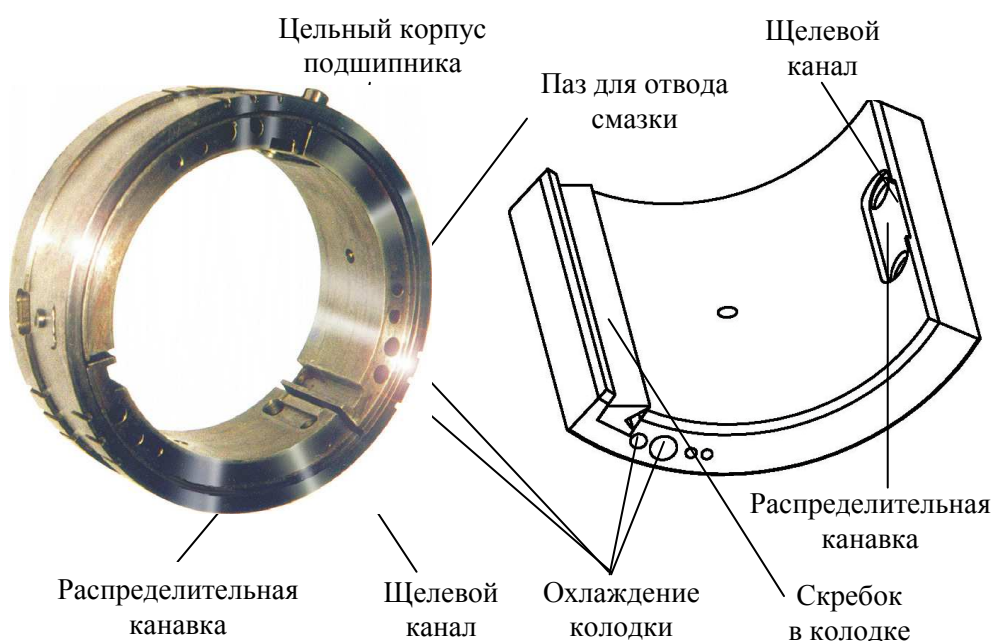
Трехсегментный демпферный подшипник на гидростатической пленке компрессора сайклинг-процесса
